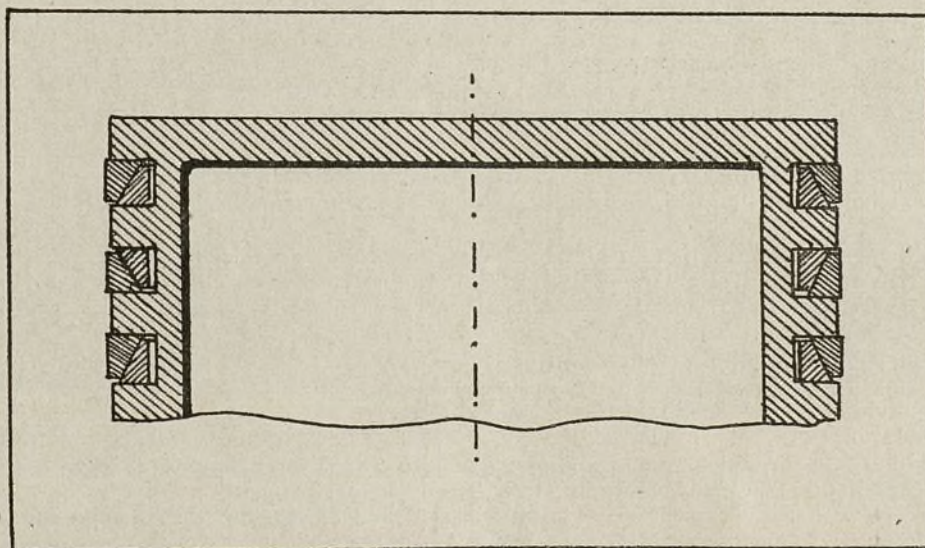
Disposición de los segmentos a cierre integral en un émbolo.
